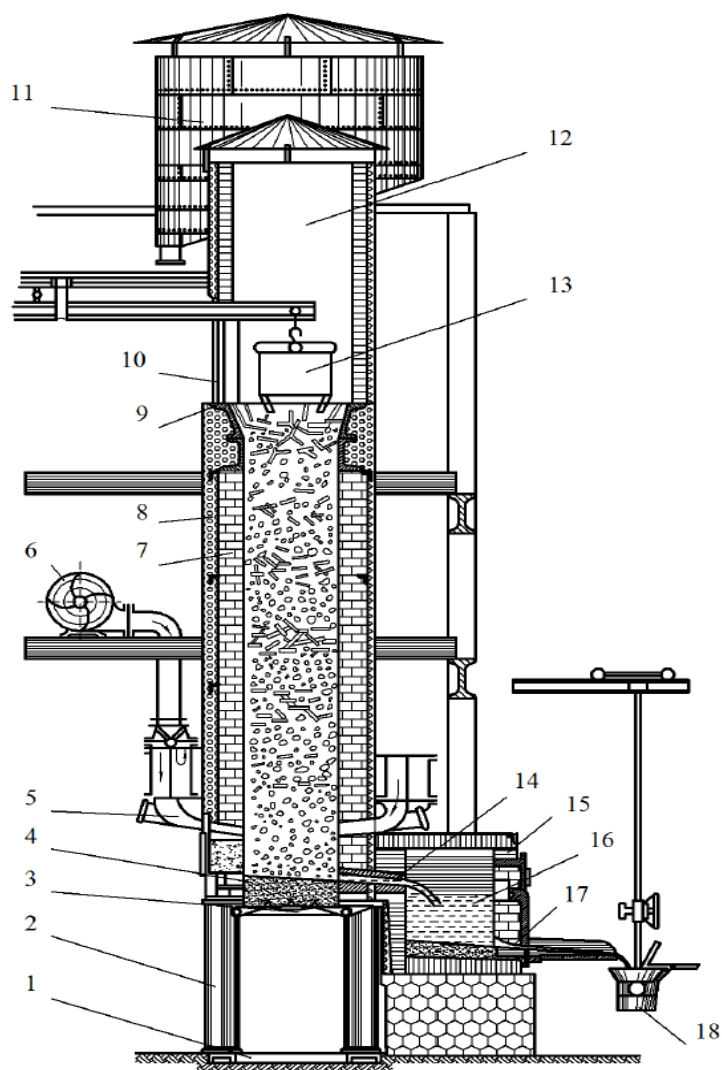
Схема устройства вагранки: 1 - фундамент; 2 - колонны; 3 - подовая плита; 4 - под (лещадь); 5 - фурмы; 6 - вентилятор; 7 - футеровка; 8 - кожух; 9 - плиты колошника; 10 - загрузочное окно; 11 - искрогаситель; 12 - шахта; 13 - бадья; 14 - чугунная летка; 15 - копильник; 16 - жидкий чугун; 17 - выпускная летка копильника; 18 - ковш раздаточный
